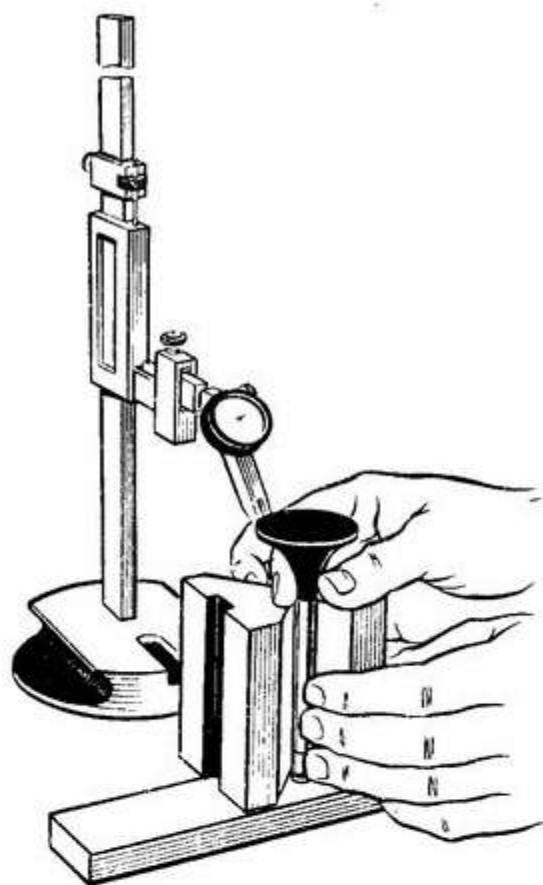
Проверка concentричности рабочей фаски клапана относительно стержня
